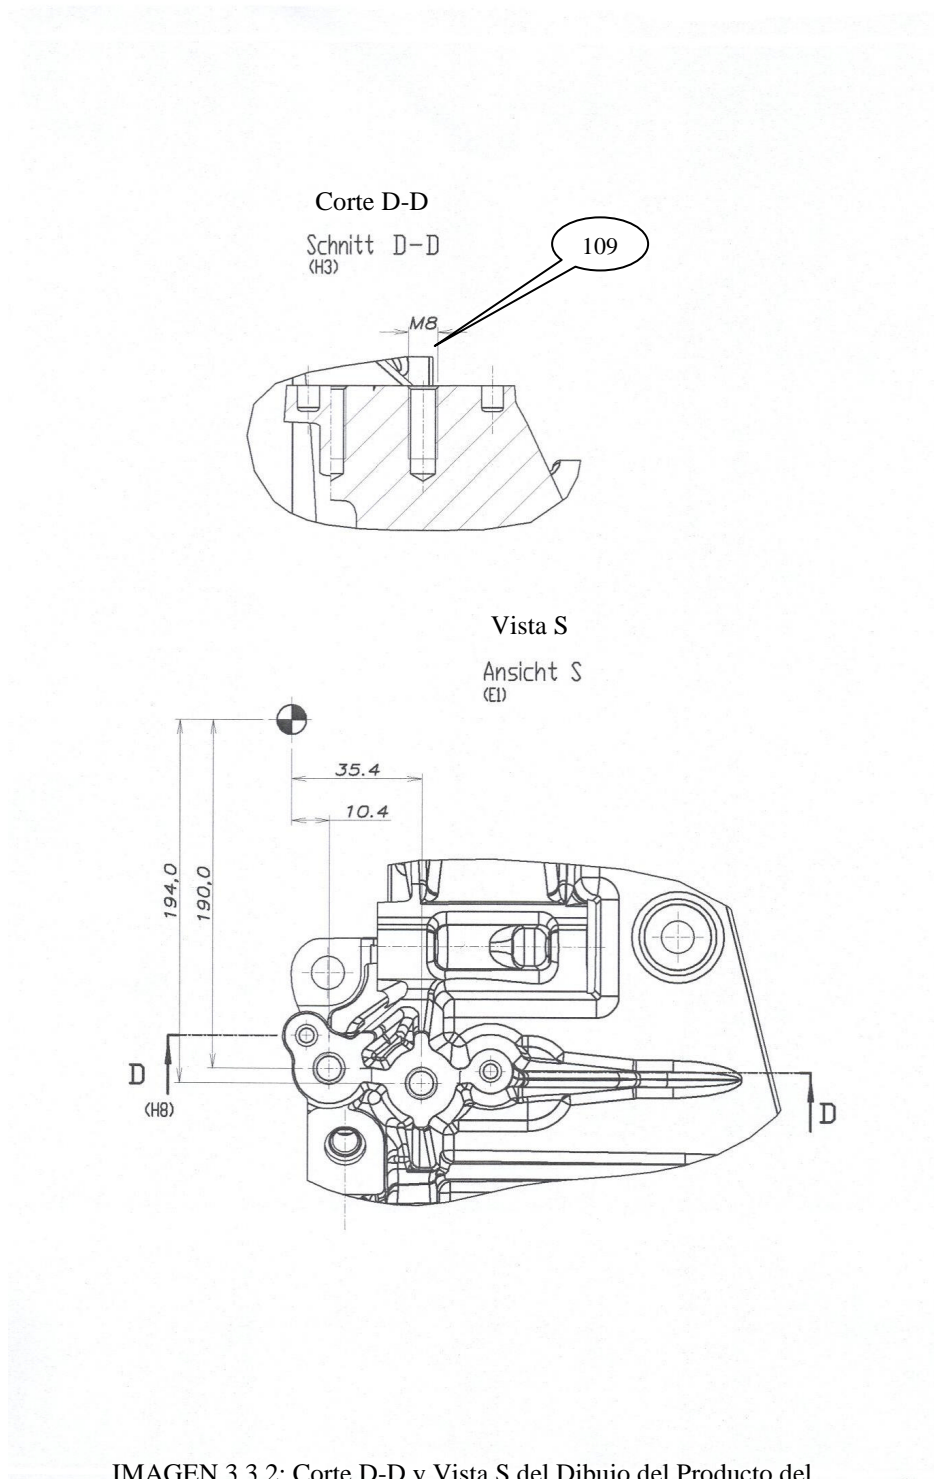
Corte D-D y Vista S del Dibujo del Producto del Soporte de Agregados de Motor.
